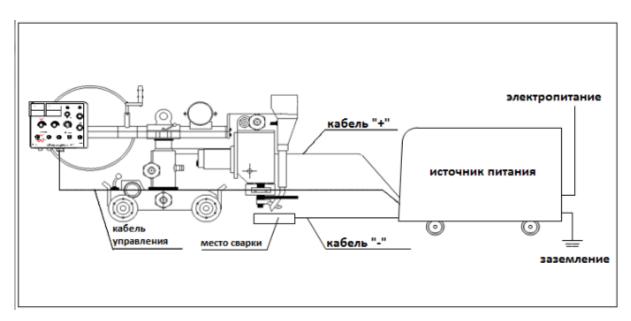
Соединения сварочной системы Pandaweld 1250 [6].
